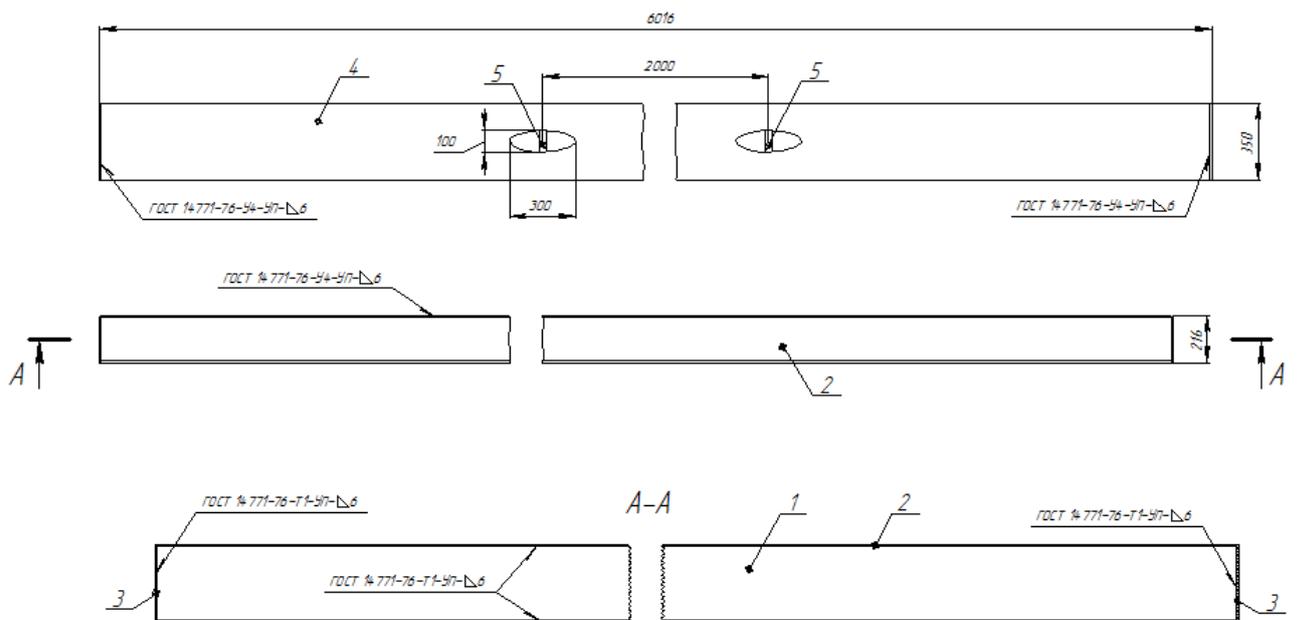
Чертеж откидного борта с отверстиями для пуансонов
